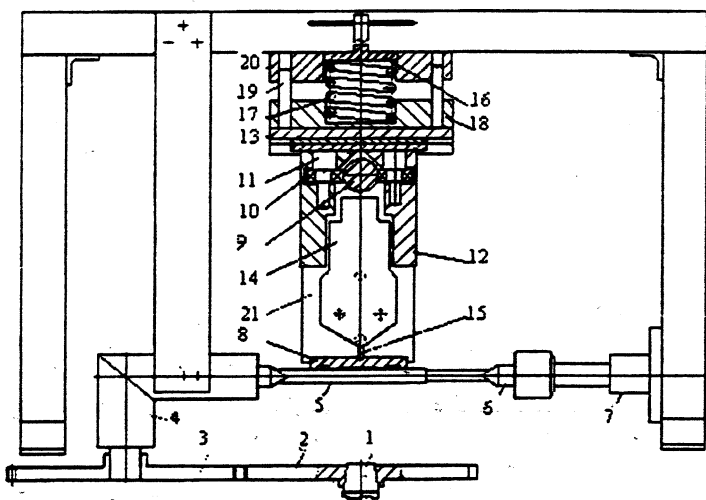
Схема устройства для притирки цилиндрических поверхностей.
